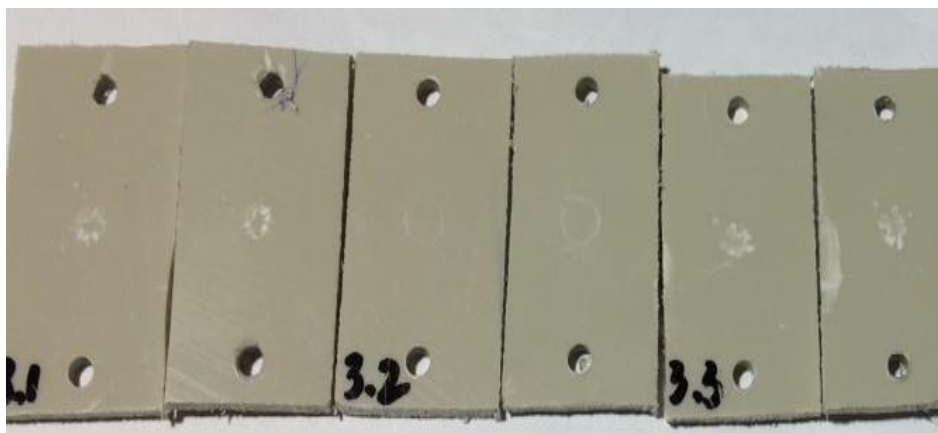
След сварного шва на полипропилене; время сварки (1,2-1,8) с
